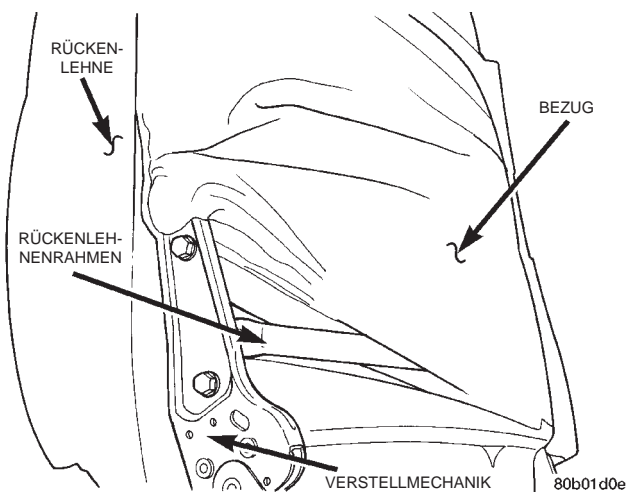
Obere Halterung der Rückenlehnen-Verstellmechanik aus- und einbauen
